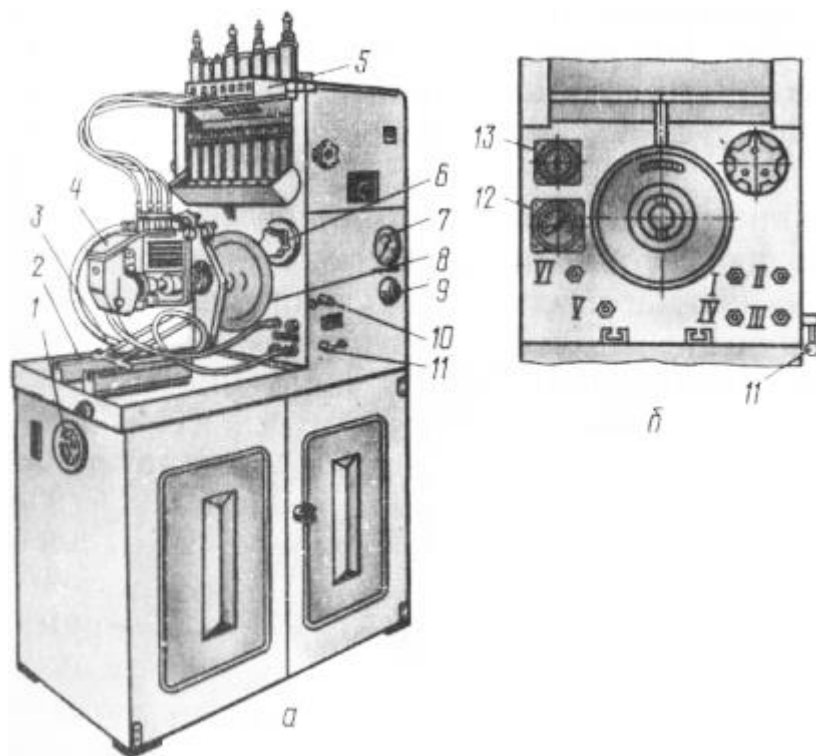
Проверка топливного насоса на стенде КИ-921М: а - общий вид стенда; б - расположение приборов и штуцеров на передней панели стенда; 1 - рукоятка регулировки частоты вращения вала привода; 2 - направляющие стола; 3 - кронштейн для крепления проверяемого насоса; 4 - топливный насос; 5 - кронштейн сливных лотков; 6 - рукоятка счетчика частоты вращения кулачкового вала насоса; 7 и 12 - манометры; 8 - неподвижный диск; 9 - рукоятка дросселя; 10 - рычаг включения счетчика-автомата; 11 - рукоятка распределительного крана; 13 - тахометр; 1...VI - штуцеры стенда: I - от бака; II - от фильтра стенда; III - к фильтру стенда; IV - для подпора топлива; V - для высокого давления (25 МПа); VI - для насоса двигателей Д-108 и Д-130.
